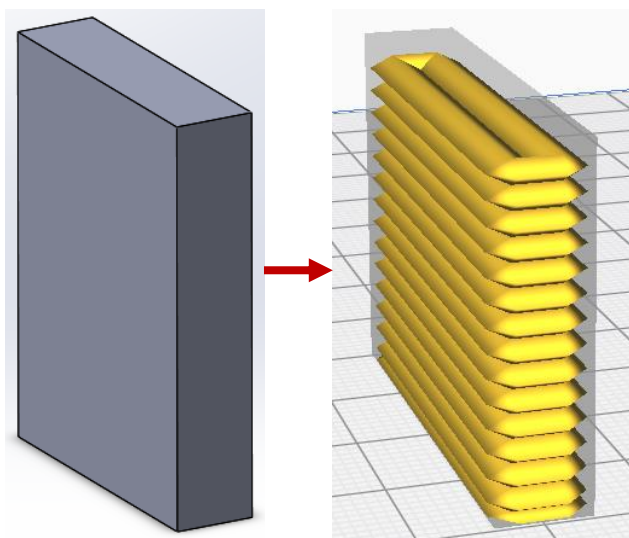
A la izquierda el CAD de partida, a la derecha, el resultado obtenido mediante el laminador.
